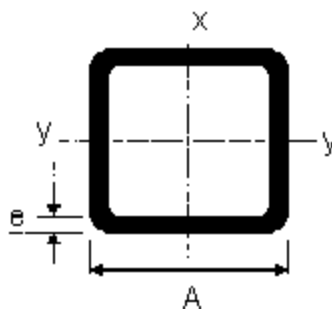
Tubo Metálico de Perfil Quadrado Conforme Norma NBR 8261
